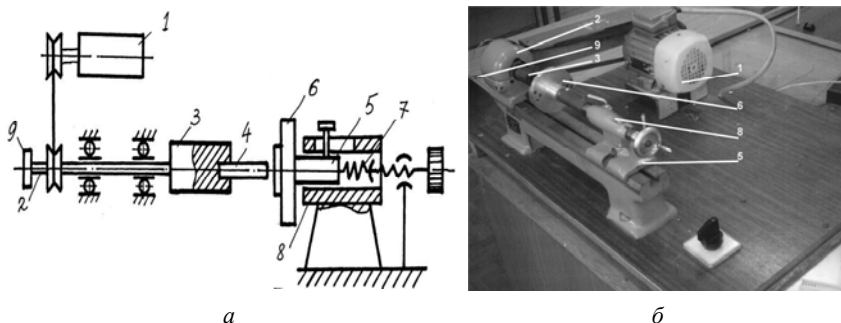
Лабораторная установка для сварки пластмасс трением:
